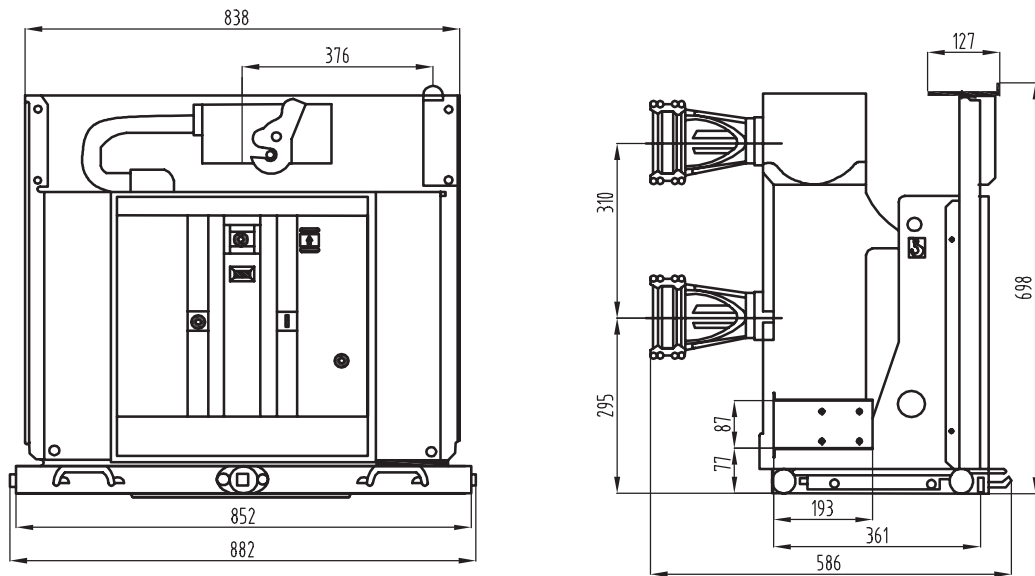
Габаритный размер выключателя ВВ-12 выкатного исполнения для ячейки шириной 1000 мм
